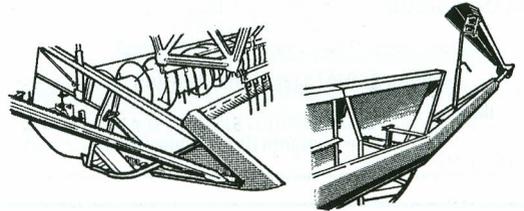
Plataforma de corte com dedos levantadores. Detalhe do dedo levantador.
